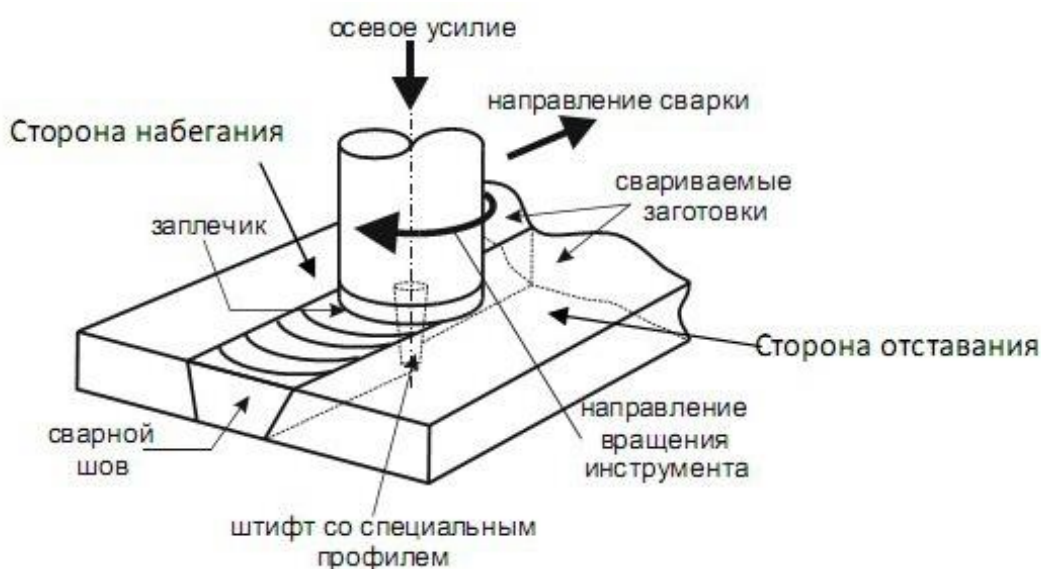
Схема процесса сварки трением с перемешиванием
